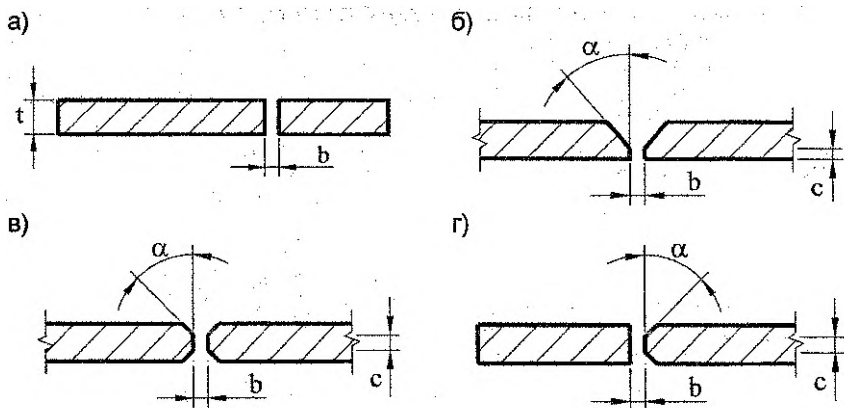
Форма подготовки кромок свариваемых элементов:
